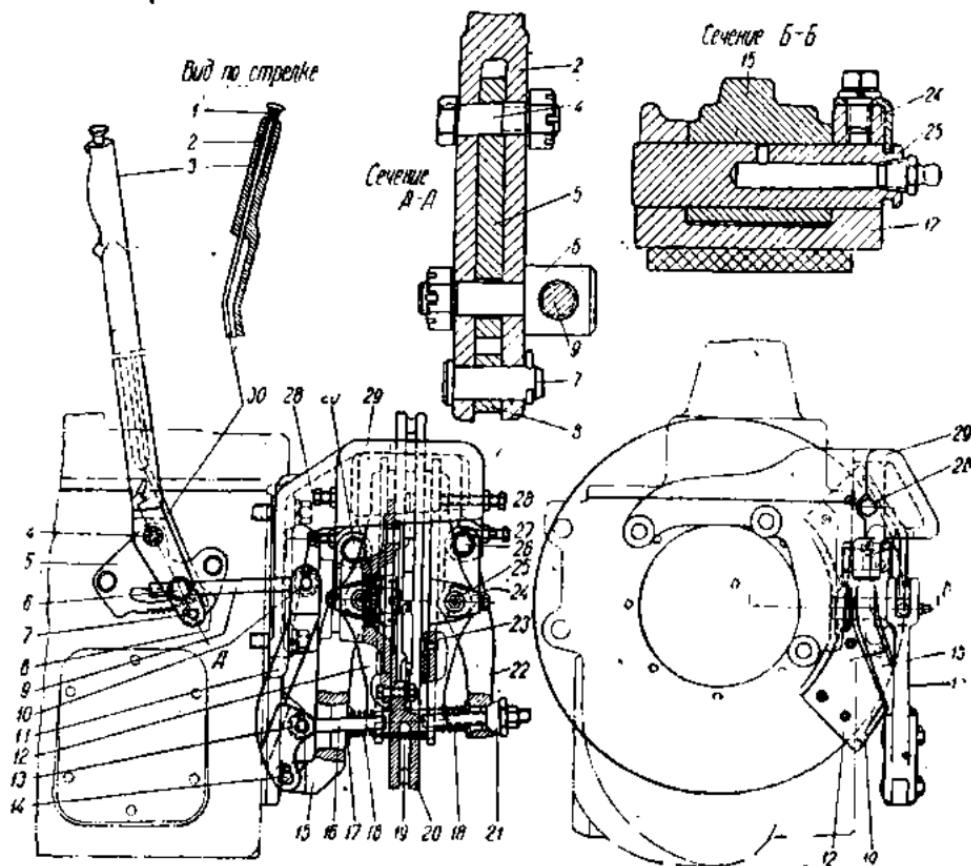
Ручной (центральный) тормоз. (3 — рычаг; 5 — сектор; 9 — тяга; 11 — рычаг управления колодками; 15 — кронштейн; 16 — соединительная тяга; 17 — шайба; 18, 19 — пружины; 20 — диск тормоза; 21 — регулировочная гайка; 22 — рычаг правой колодки; 23 — фрикционная обшивка; 27 и 28 — регулировочные болты).
